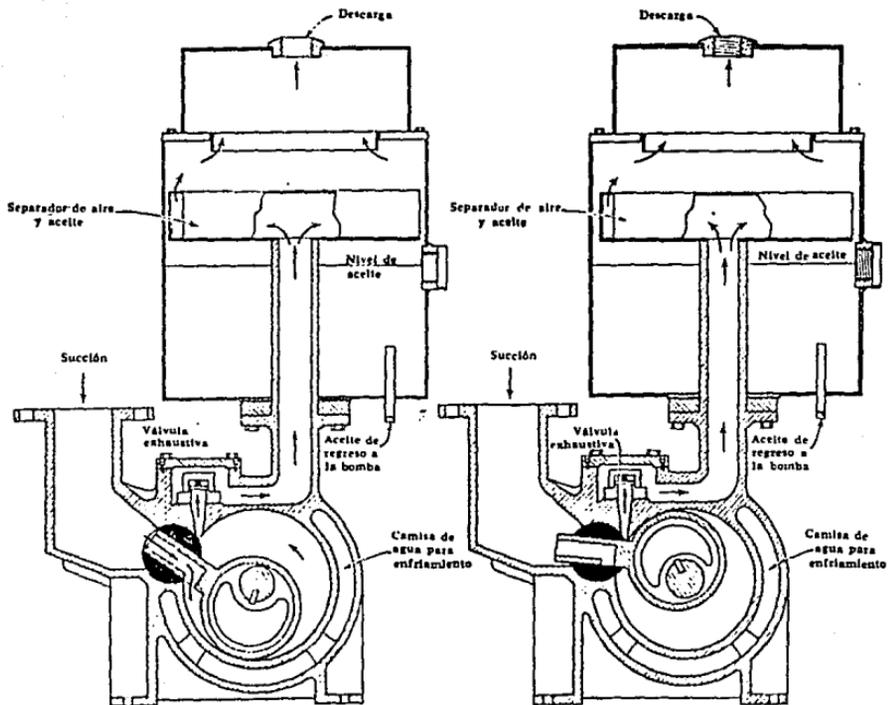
Corte de una bomba rotatoria de pistón y su ciclo de operación.
